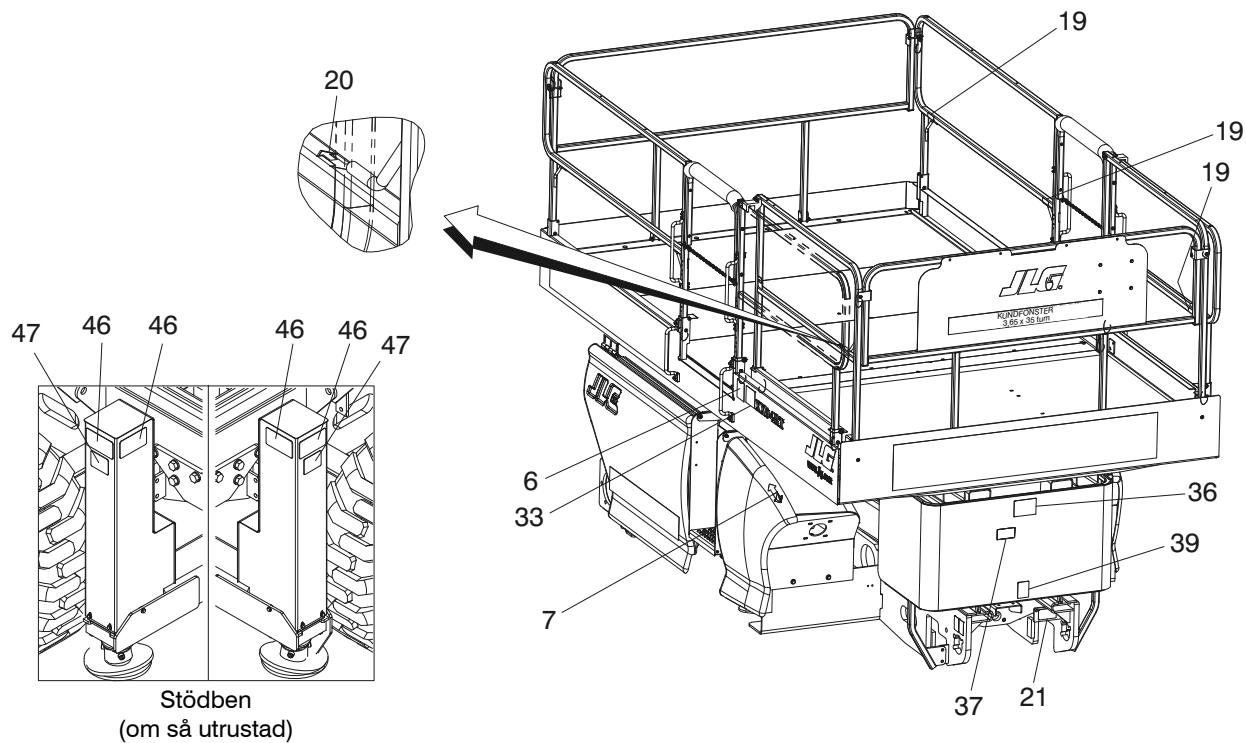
Placering av dekaler – blad 2 av 2 (CE/AUS)
